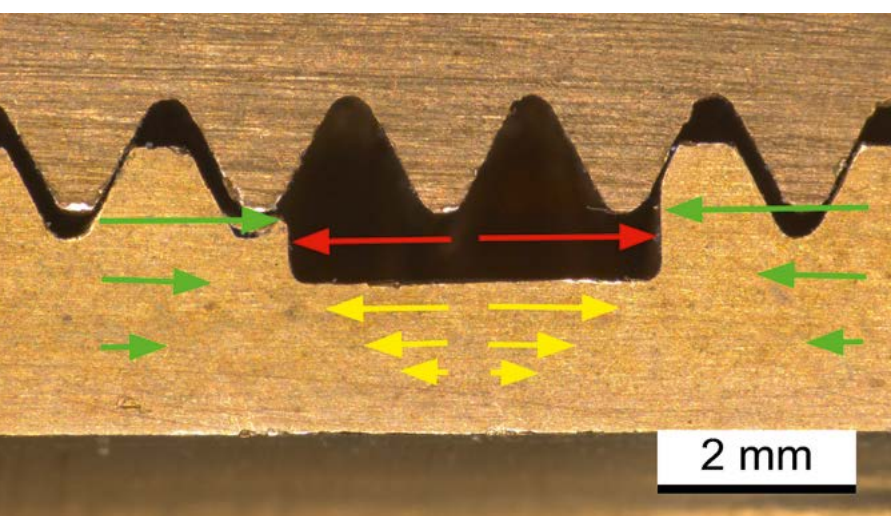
/ Die Gewindeverbindung – hier ohne Dichtring – im Querschnitt: Durch die Komprimierung des Dichtrings drückt dieser unter anderem gegen die Flanken der Nut (rote Pfeile) und erzeugt somit im Nutbereich Zugspannungen (gelbe Pfeile). Durch das Einschrauben deutlich über den Dichtring hinaus werden diese Zugspannungen durch das Gegengewinde aufgenommen (grüne Pfeile).
